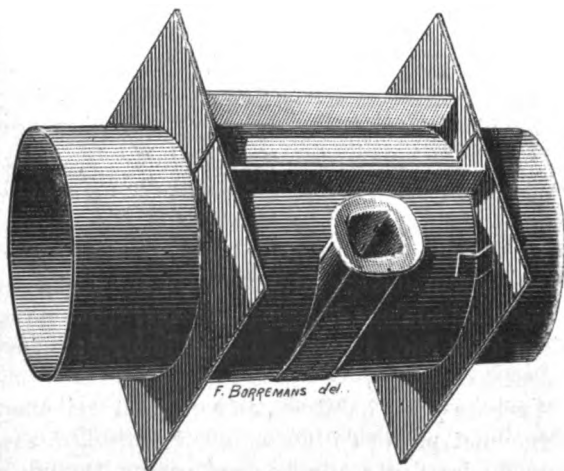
Soudure des gros tubes ; dispositif avant la coulée.
